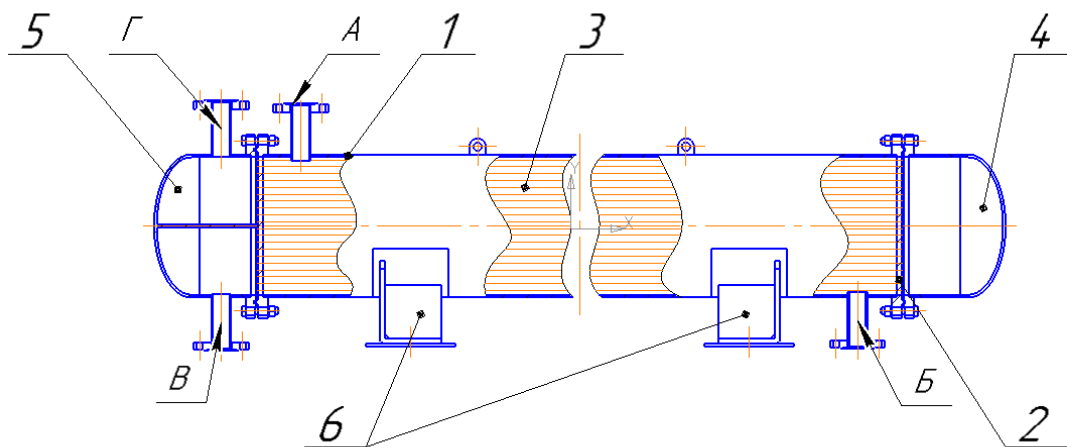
Кожухотрубний теплообмінник з нерухомими трубчастими решітками
